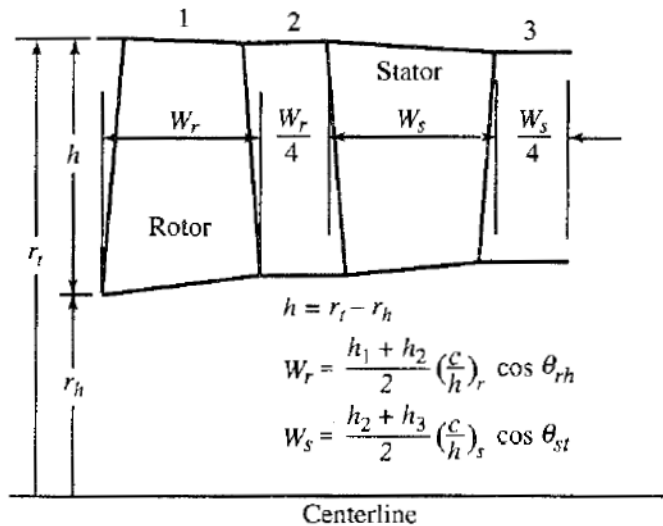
Dimensiones axiales de un escalón de compresor axial [6]
